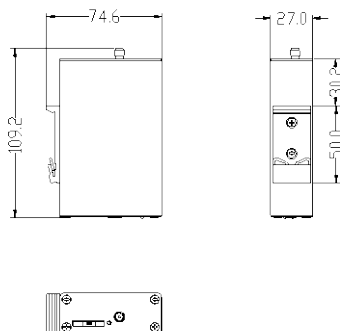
Габаритные размеры для модели IP20 (корпус на на DIN-рейке)
